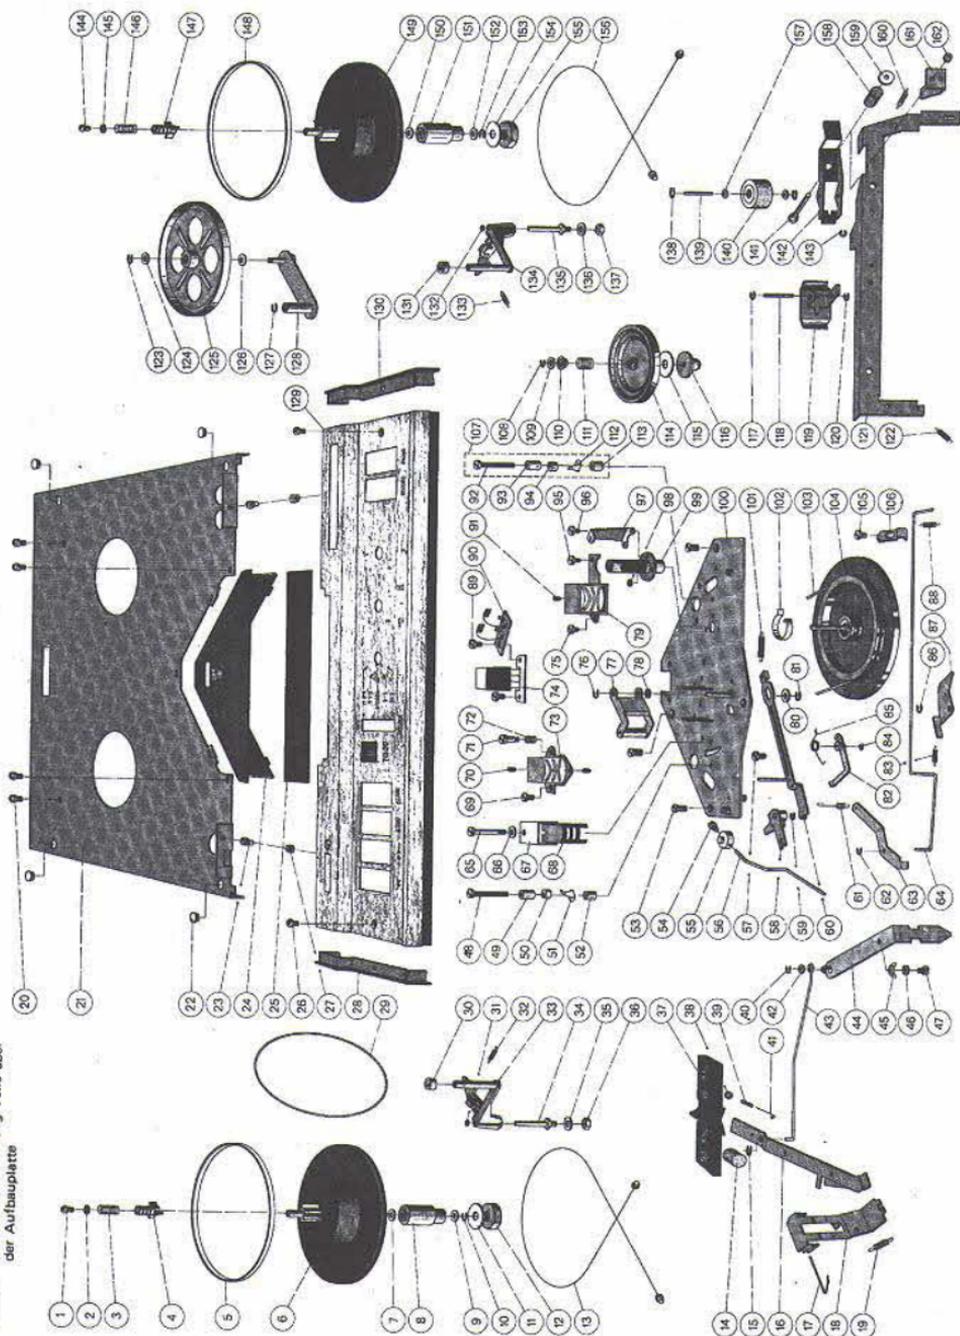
Explosionsdarstellung Teile unter der Aufbauplatte
